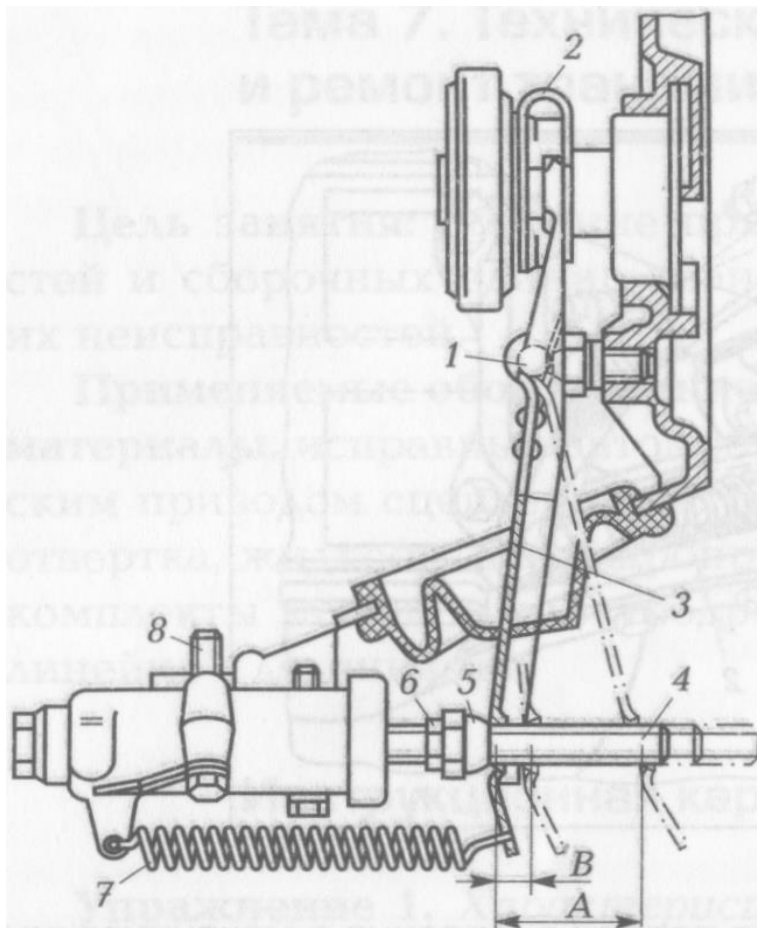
Регулировка свободного хода педали сцепления с гидравлическим приводом: 1 — шаровая опора; 2 — пружина; 3 — вилка выключения сцепления; 4 — шток; 5 — регулировочная гайка; 6 — контргайка; 7 — оттяжная пружина; 8 — штуцер; А и В — соответственно полный и свободный ход рычага
